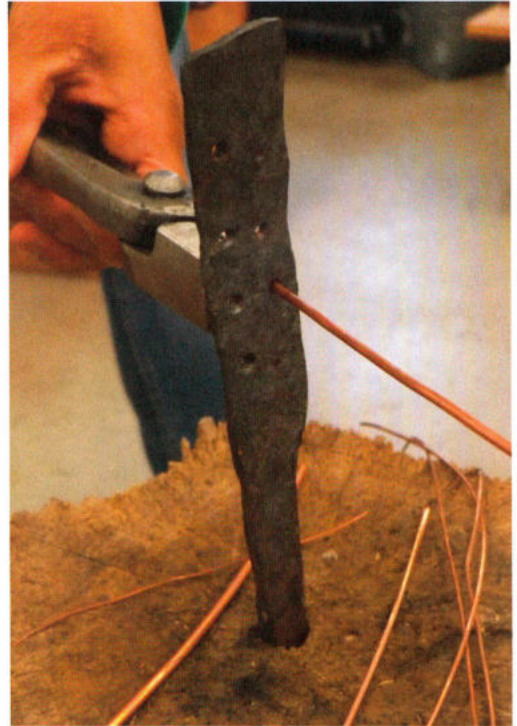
Drahtziehen am eingelassenen Zieheisen. – Wire drawing with fixed iron drawplate.
